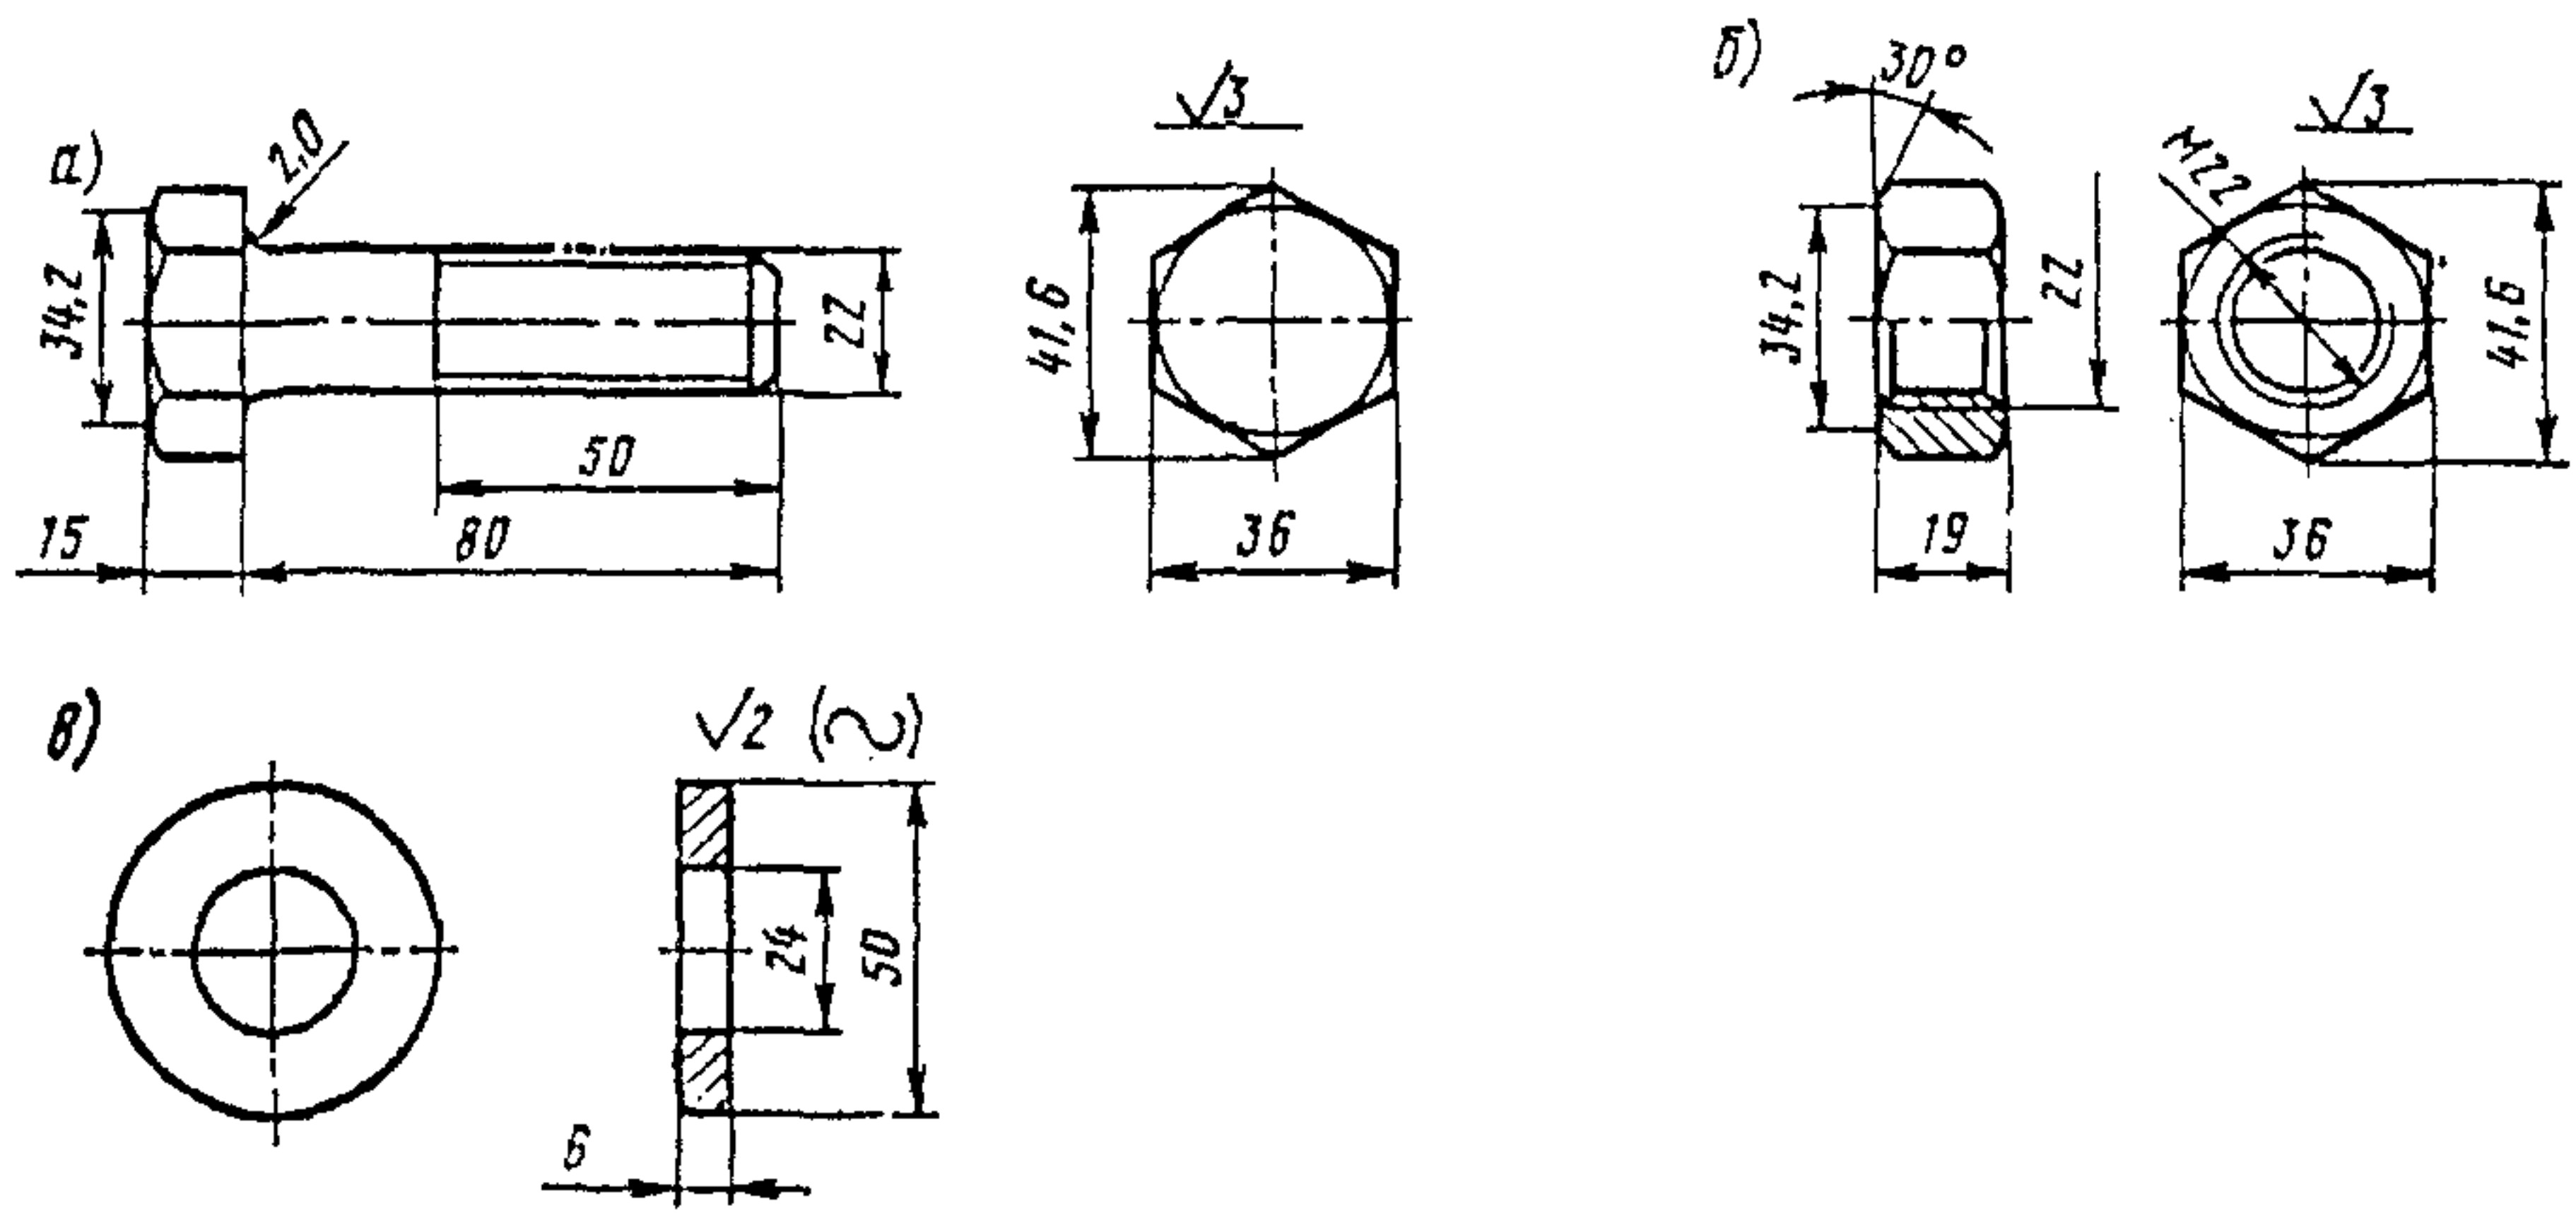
Болт для прикрепления охранных приспособлений к металлическим поперечинам
